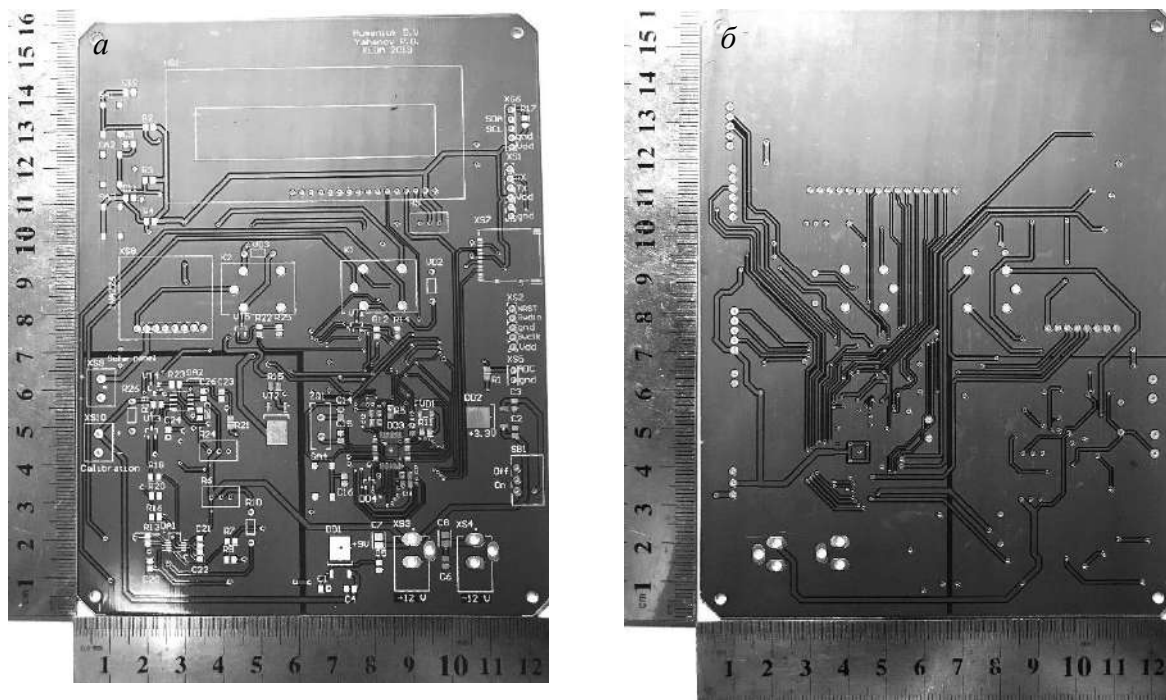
Фото виготовленої друкованої плати, а – вид зверху, б – вид знизу
